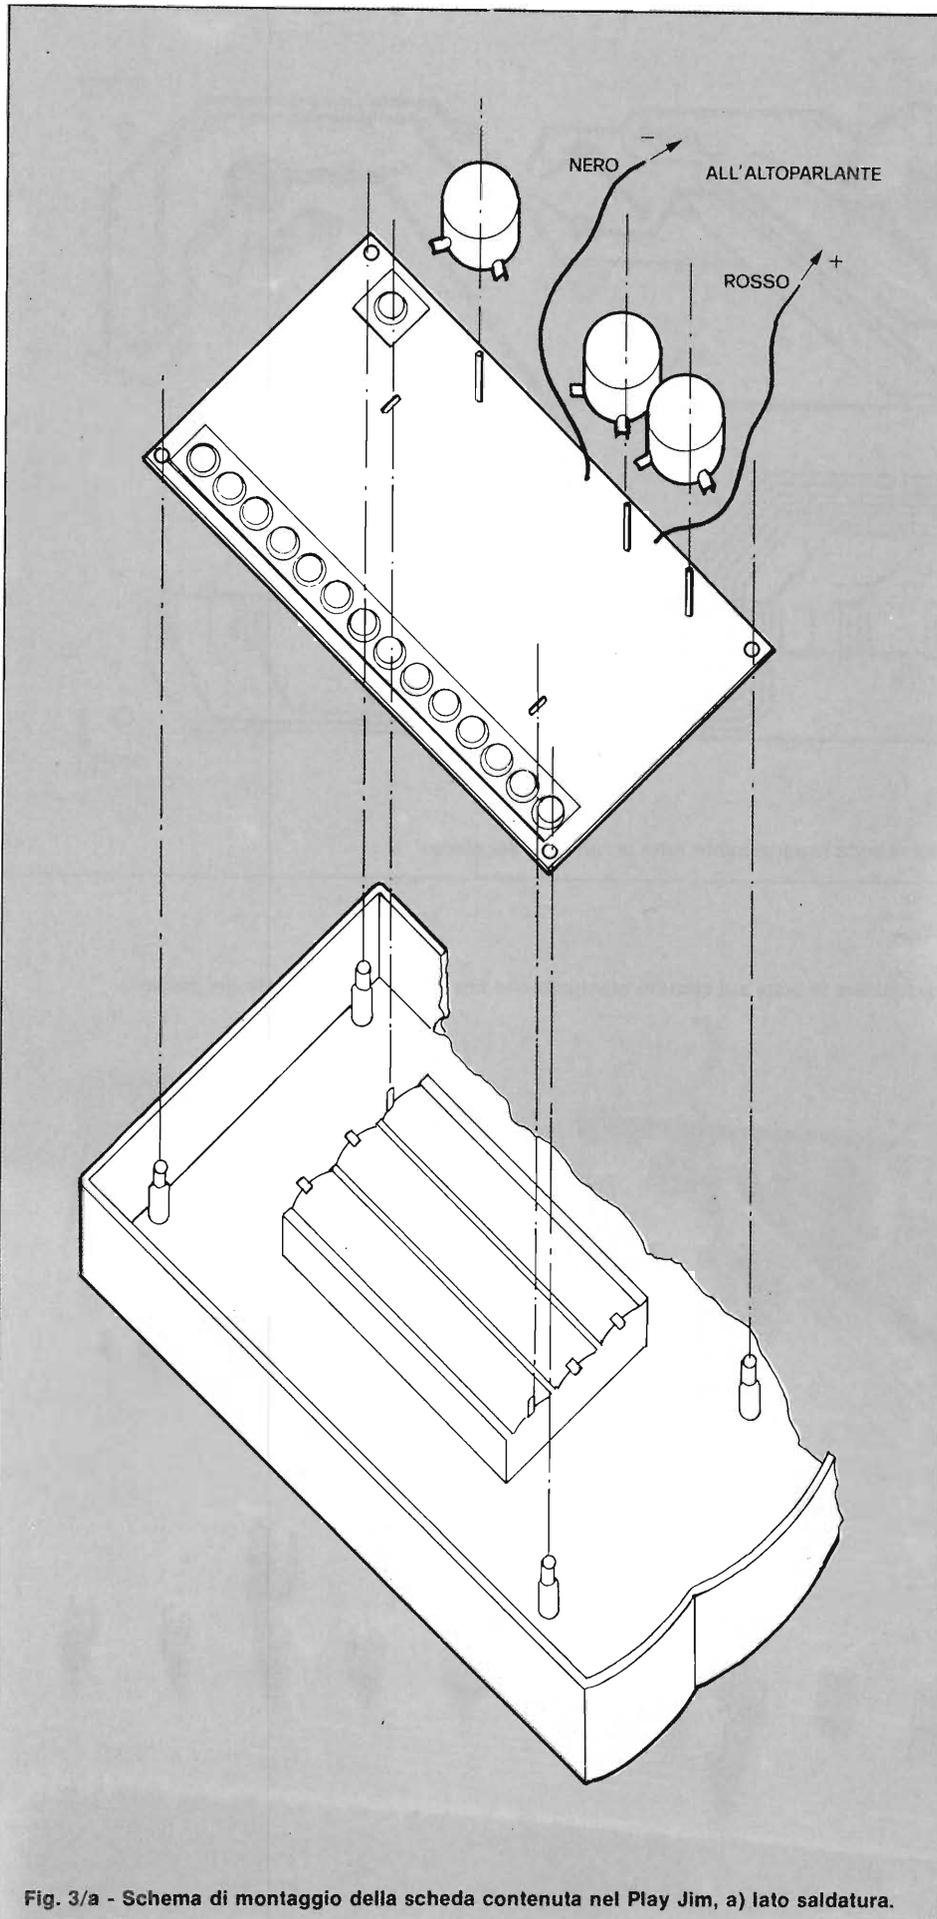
/a - Schema di montaggio della scheda contenuta nel Play Jim, a) lato saldatura.
